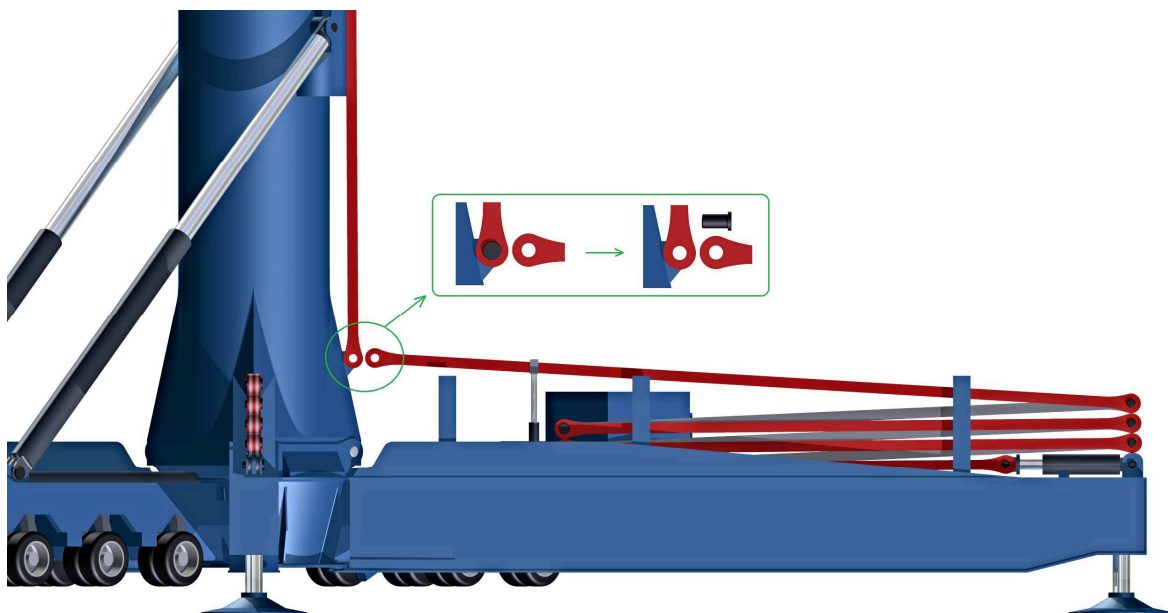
Pomocný hydraulický válec určený k přizvednutí horní části výztuže do montážní polohy.
